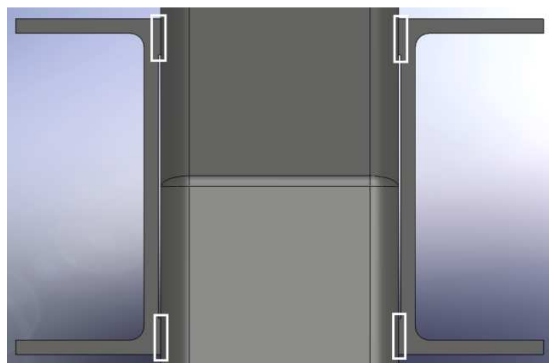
Localização das soldaduras dos perfis U's
